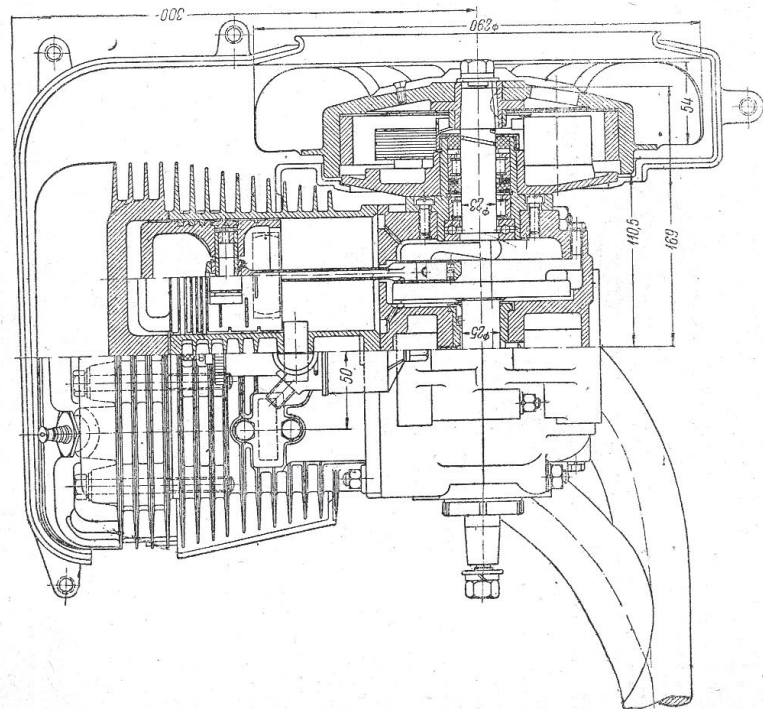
Габаритные размеры двигателей „Блэкберн“ 250 см^3 (63 \times 79).
